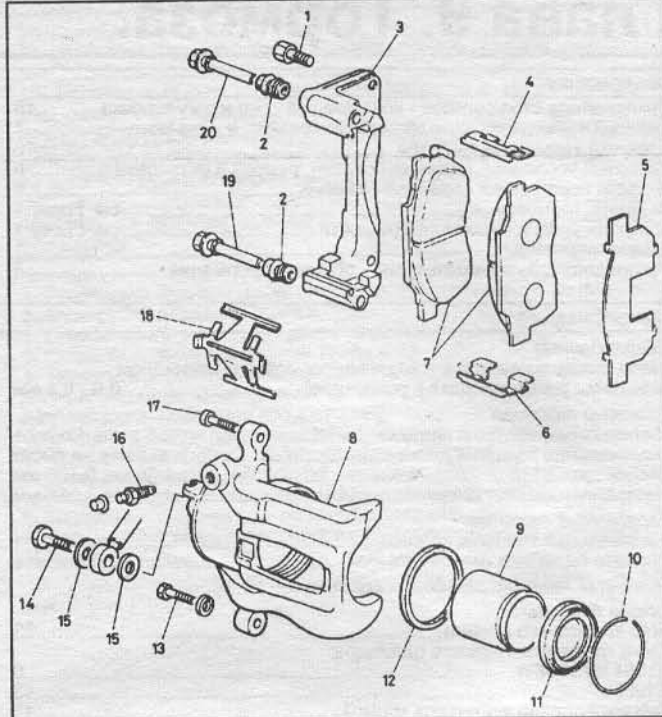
в Сборка переднего тормоза фирмы Nissin: 1 - болт направляющей; 2 - пыльник; 3 - направляющая; 4 - фиксатор колодок; 5 - толкатель колодок; 6 - фиксатор; 7 - колодка; 8 - суппорт; 9 - поршень; 10 - кольцо пыльника; 11 - пыльник; 12 - уплотнение; 13 - болт направляющей; 14 - болт банджо; 15 - уплотняющие шайбы; 16 - штуцер прокачки; 17 - болт суппорта; 18 - держатель; 19, 20 - втулки направляющей.
